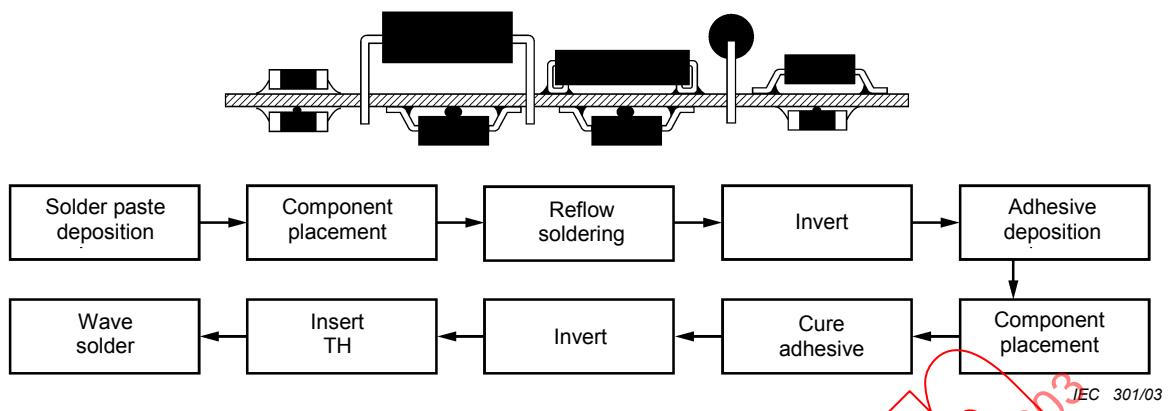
Montage par technique combinée, manuel et refusion double face
